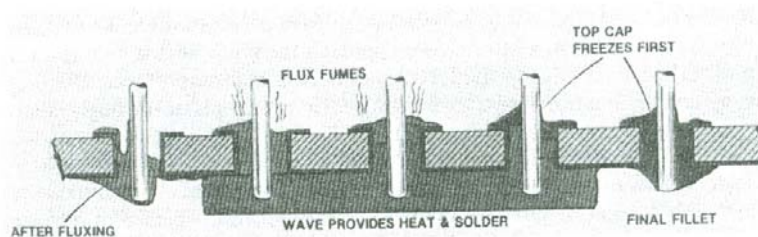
Esquema que ilustra el impacto de la ola de soldadura en una tarjeta doble capa.
